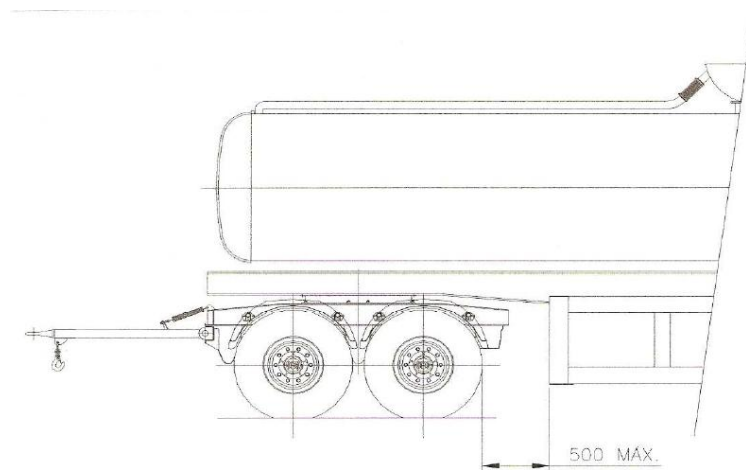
Posição da aresta frontal em veículo rebocado de carga – Vista lateral (dimensões em mm)
